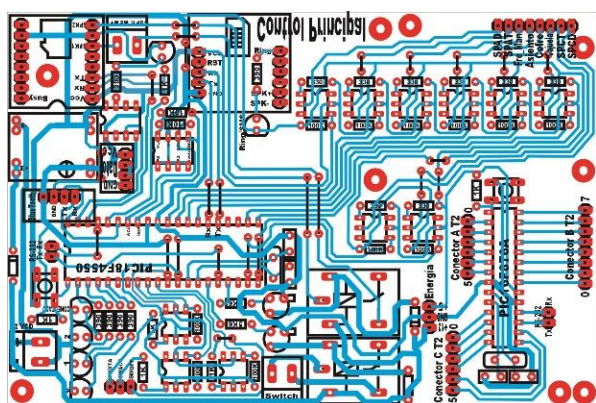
Diseño de PCB del circuito principal para el sistema de control Principal
